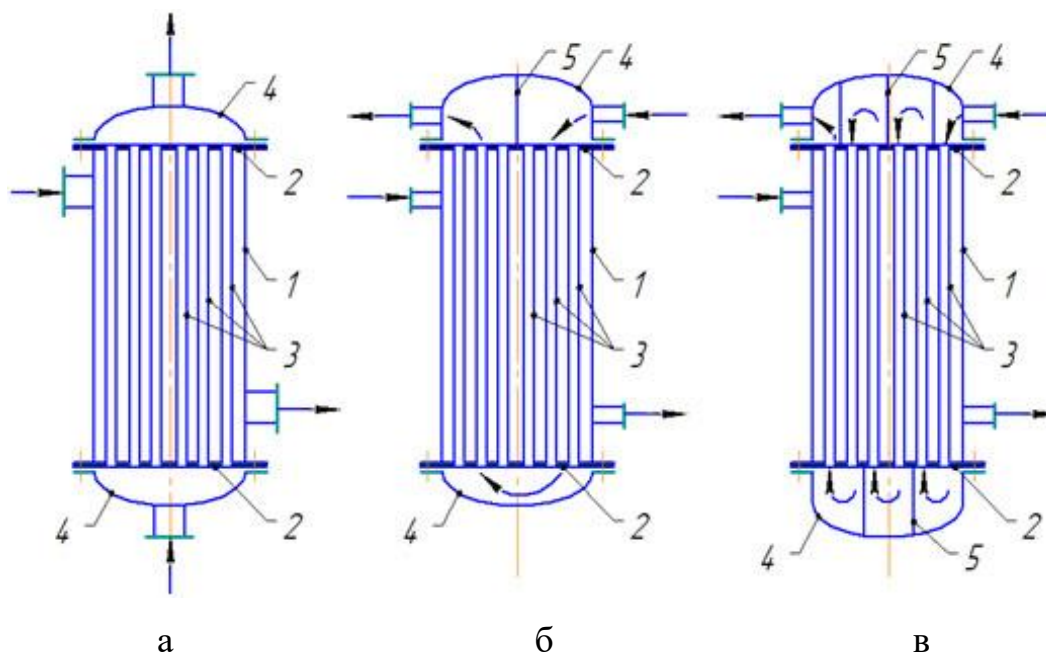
Кожухотрубчатые теплообменники с неподвижными решетками: а – одноходовой; б – двухходовой; в – шестиходовой: 1 – корпус; 2 – трубные решетки; 3 – трубы; 4 – крышки; 5 – перегородки
